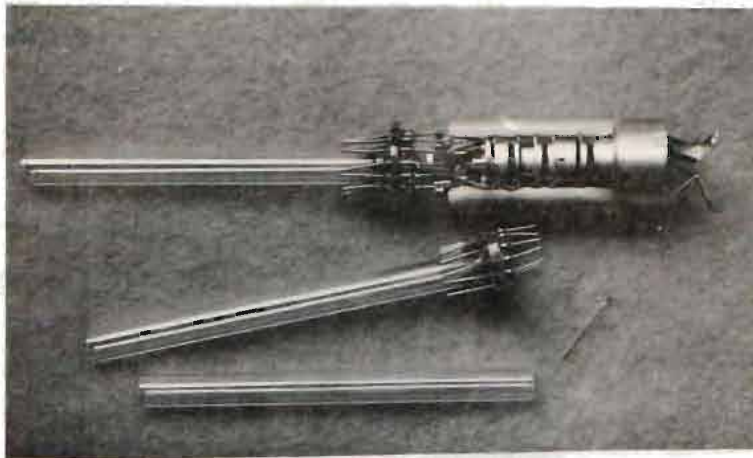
Tubulación. Fundido del tubo y colocado de arillo y terminales.
